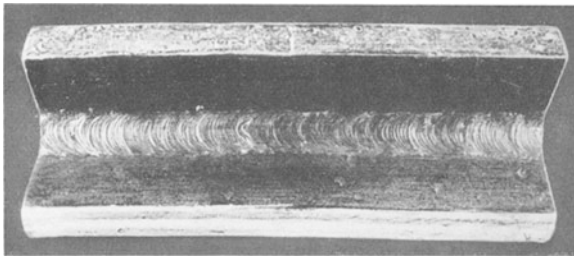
Aussehen einer Kehlschweißung.
